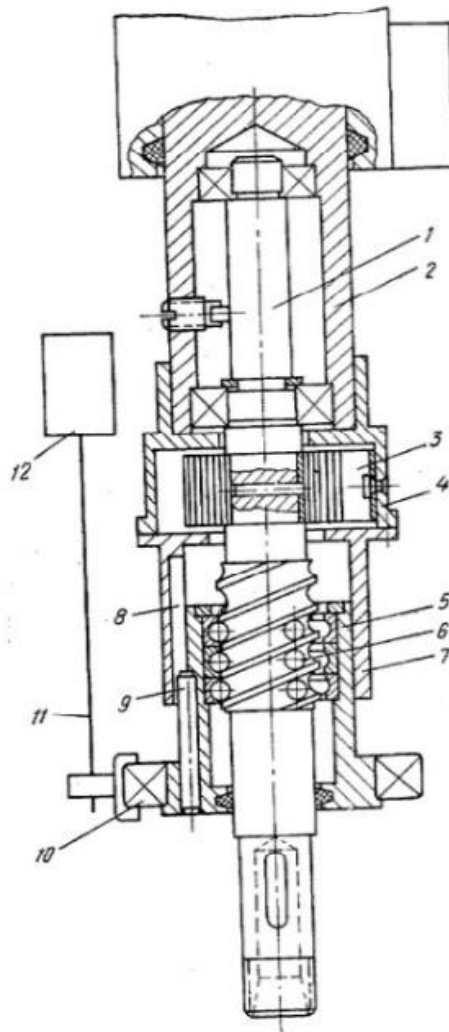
4 Шпиндель свердлильного верстата. [10]
